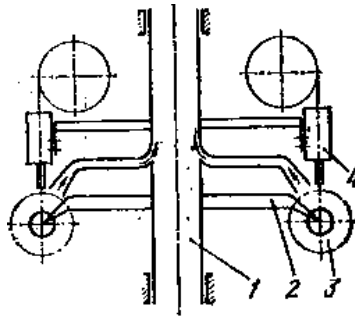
Роторный автомат для сборки и сварки тракторных катков
